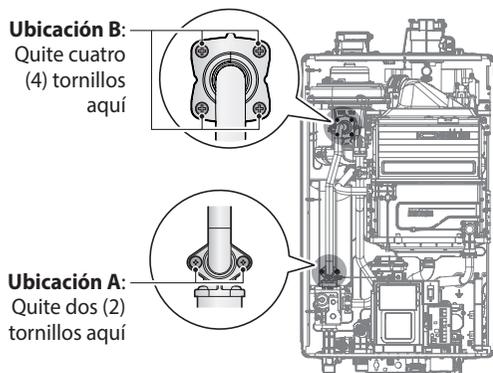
Separación de la válvula de gas del tubo de entrada de gas y el conjunto del motor del ventilador
